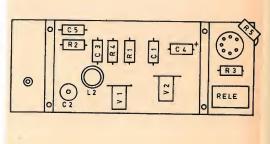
Disegno indicativo della disposizione dei componenti.
